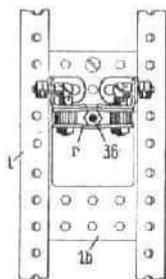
e zeigt die Befestigung der Spindelmutter an den Mülltrommelgrundplatten.
